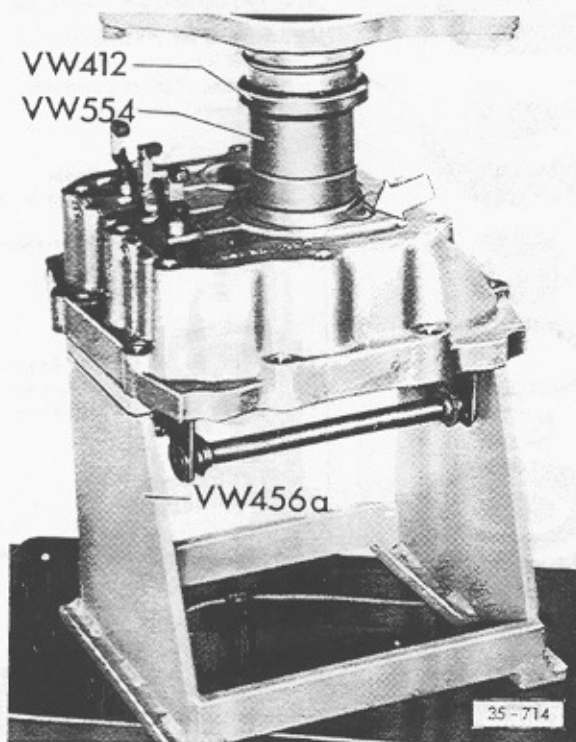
Rillenkugellager bis Anschlag in Lagerschild einpressen
